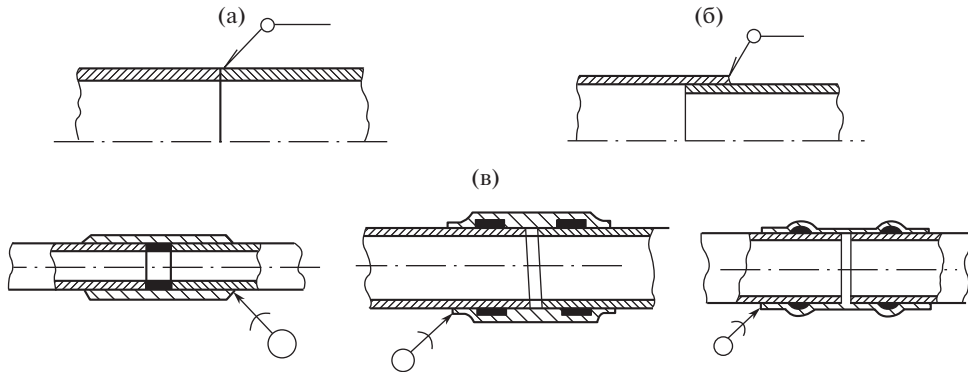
Способы сварки и пайки для соединений трубопроводов: (а) – сварное встык; (б) – сварное внахлестку; (в) – паяные соединения.
